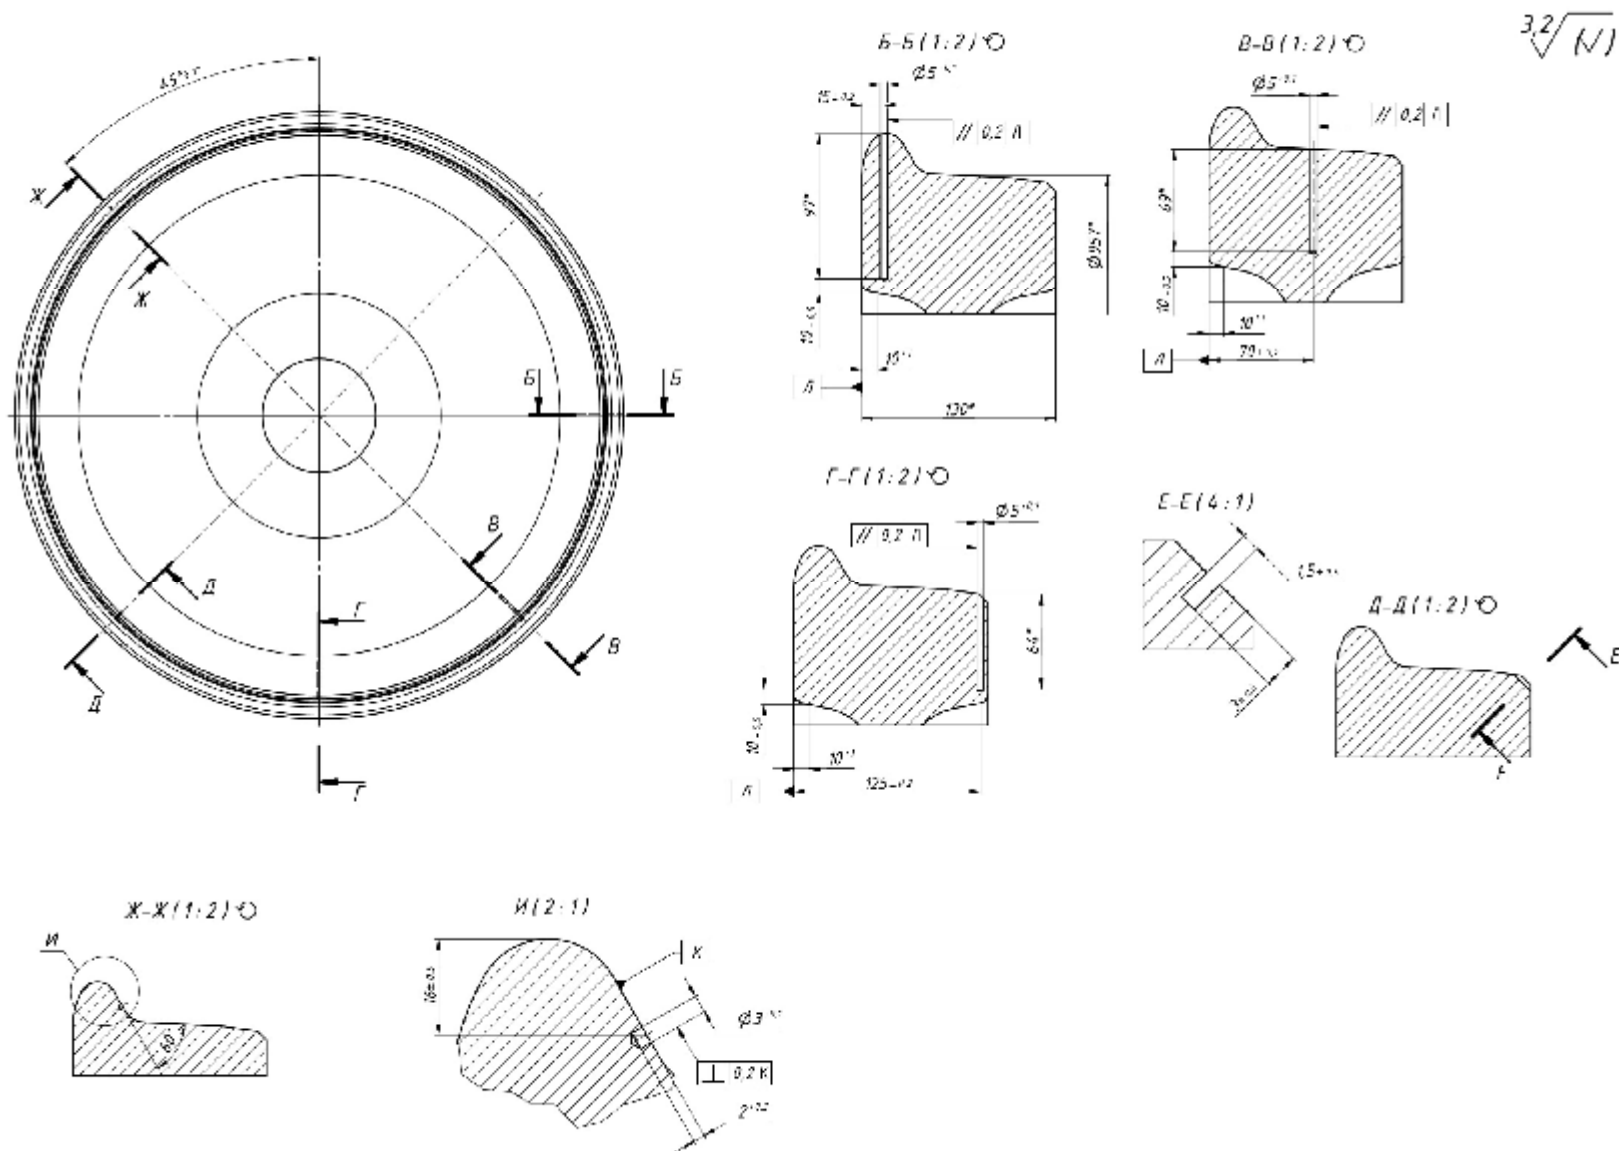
Чертеж колеса (УЗ) меры МКП-9
